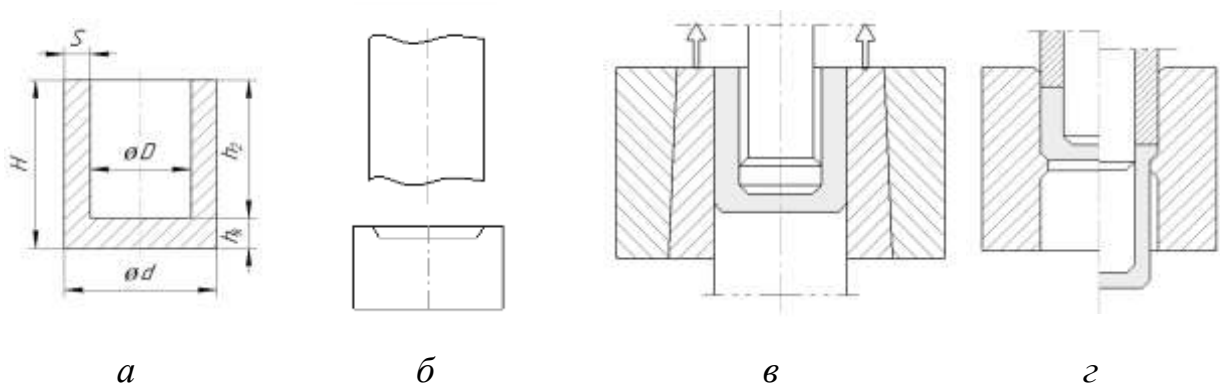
Переходи штампування деталей типу стаканів і гільз
